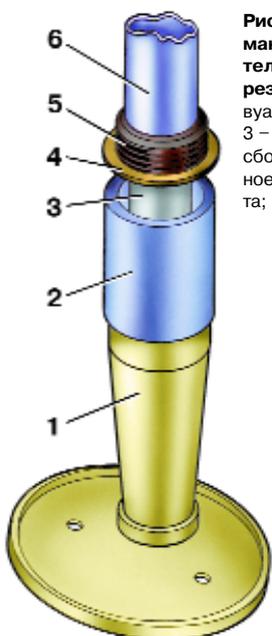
Установка манжеты с уплотнительным кольцом в резервуар: 1 – резервуар; 2 – оправка; 3 – шток с поршнем в сборе; 4 – уплотнительное кольцо; 5 – манжета; 6 – оправка
